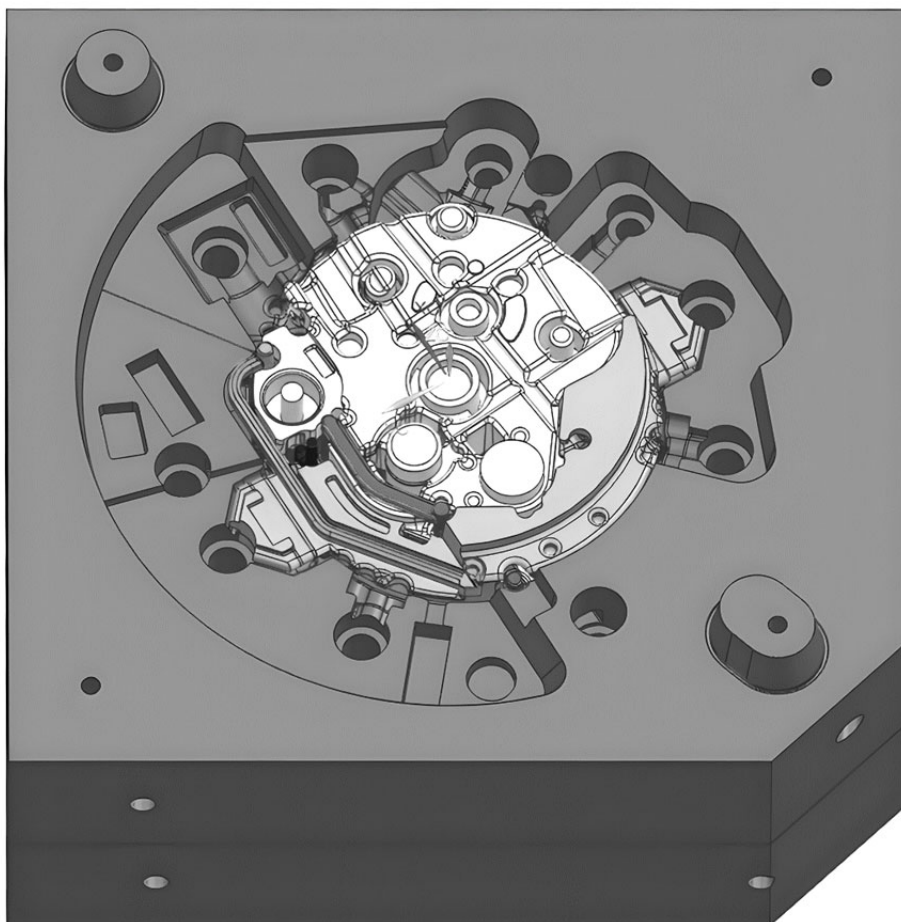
Адаптер топливных агрегатов (3D-модель отливки)
